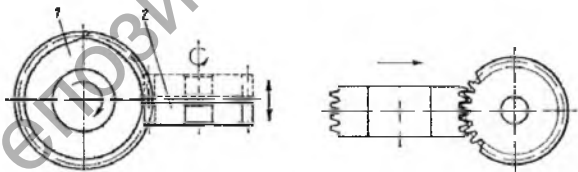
Схема шлифования зубчатых колес червячным шлифовальным кругом
